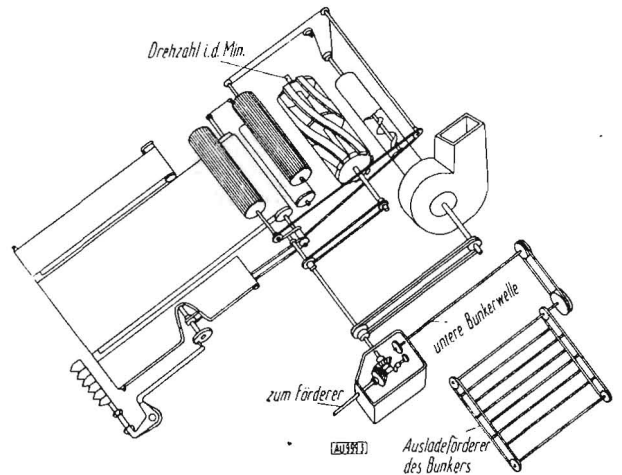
Antriebschema der Kombine SK-1, (mit Mähvorrichtung für kompakte Schnitt)
